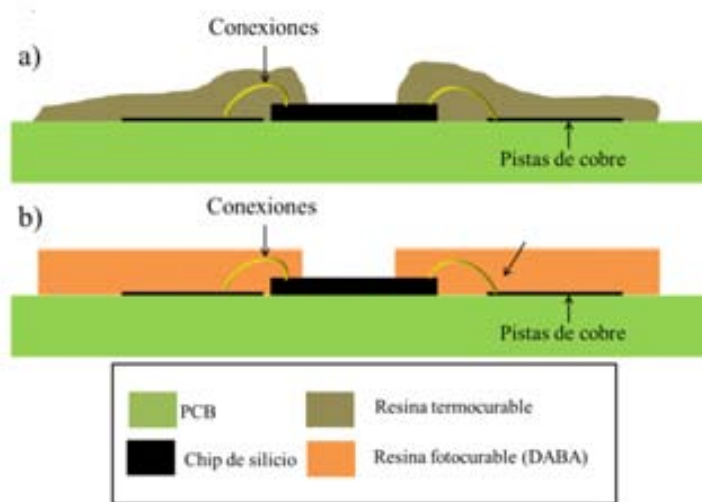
Diagrama de la sección transversal de un PCB con el chip fijado y soldadas las conexiones al PCB según la metodología *Chip on board*. Detalle de la ventana sobre la parte sensible del chip a) *glop top* de una resina termocurable y b) la resina fotocurable DABA.
